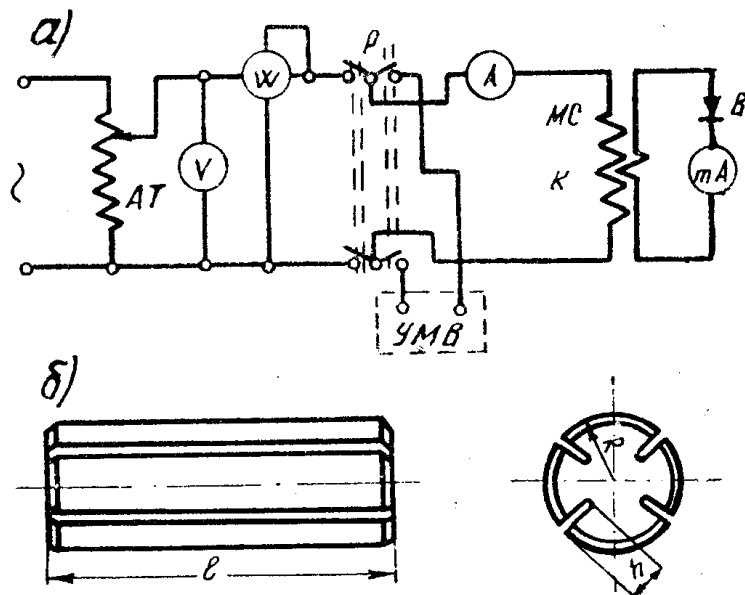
Схема включения приборов—а и внешний вид бойка молотка—б.
